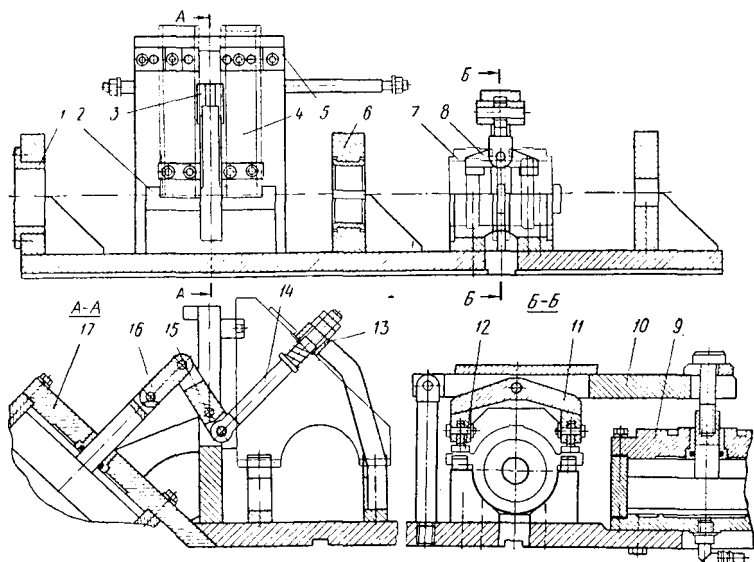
Многоместное приспособление к токарным станкам для расточных операций
